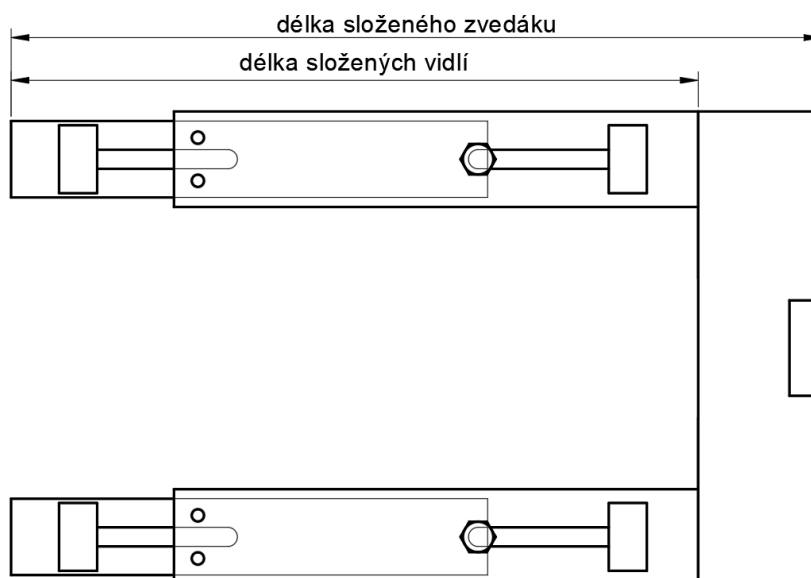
Návrh konstrukčního řešení Varianta B, pohled shora
